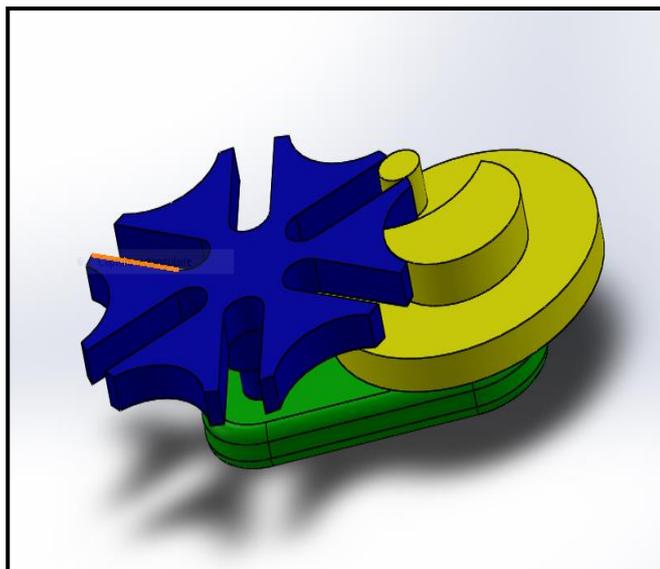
Mouvement du mécanisme et de la table index (vue 2)
